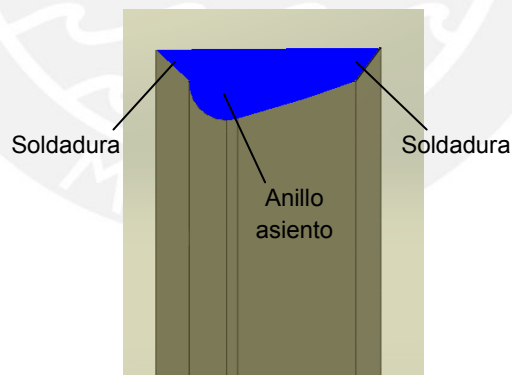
Sección transversal del anillo asiento con sus soldaduras [Material propio]
